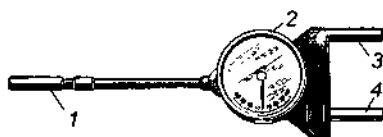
Прибор К-428 для определения углового зазора трансмиссии: 1 — рукоятка; 2 — динамометрическое устройство; 3 — неподвижная губка; 4 — подвижная губка
